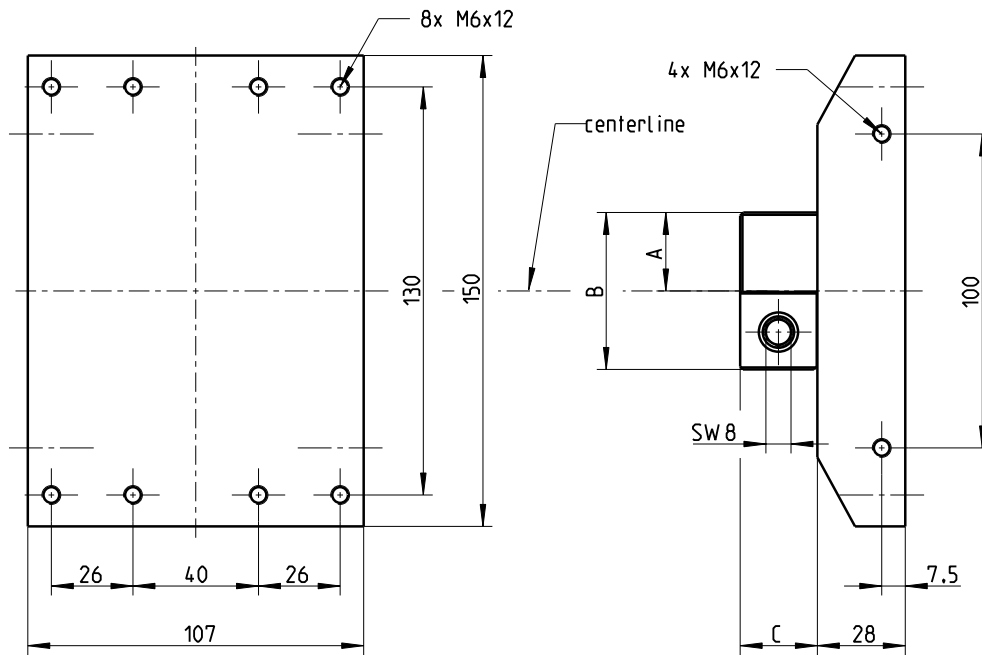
Maschinenadapter mit Spannkeil für Scheibenrevolver mit Direktwerkzeugaufnahme, Typ 9129AD...
